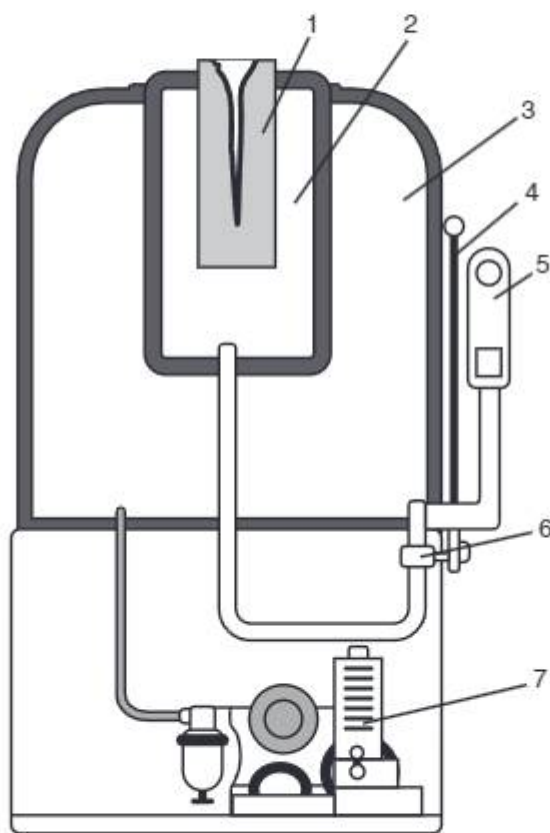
Установка «Вакуум-металл»: 1 – опока; 2 – рабочая камера; 3 – камера предварительного разряжения; 4 – рукоятка вакуумного затвора; 5 – манометр; 6 – вакуумный затвор; 7 – форвакуумный насос
